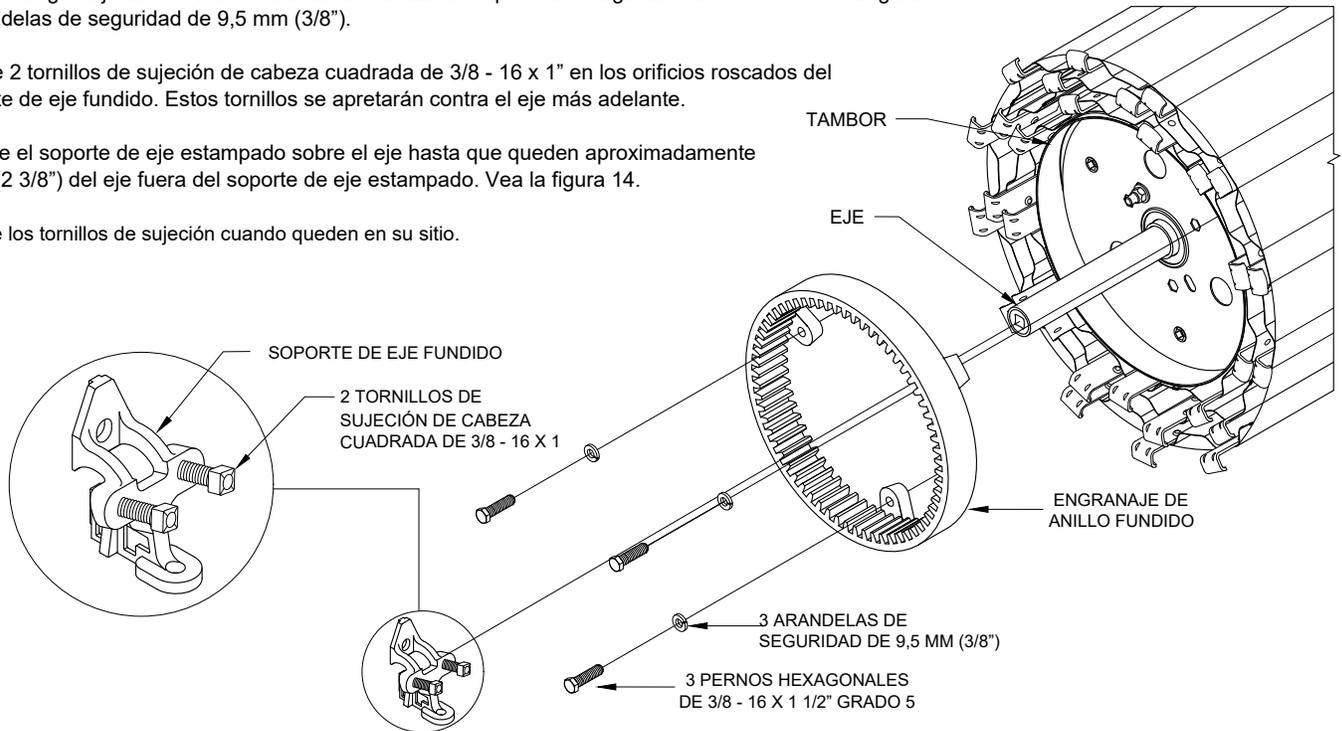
SOPORTE DE EJE FUNDIDO Y ENGRANAJE DE ANILLO FUNDIDO A CONJUNTO DE TAMBOR
